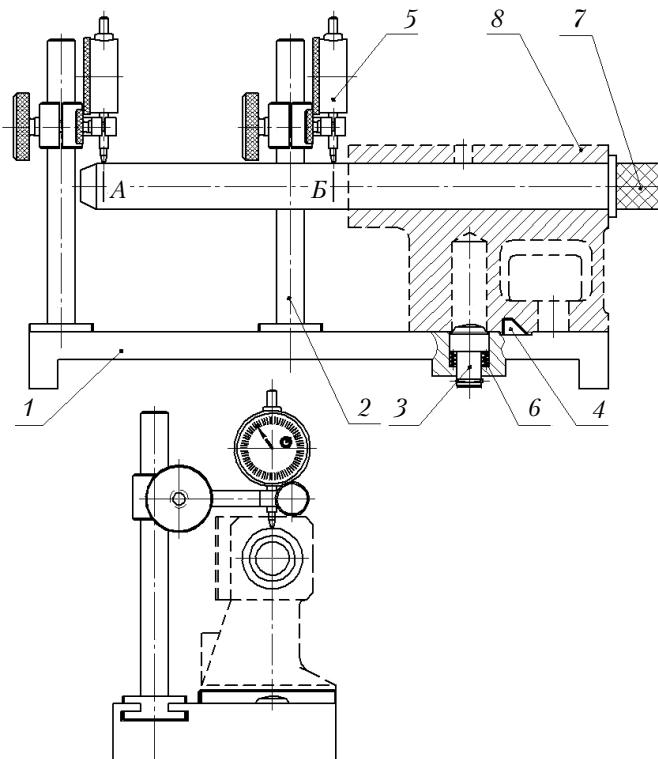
Приспособление для контроля отклонения от параллельности оси отверстия корпуса задней бабки ее установочной плоскости
